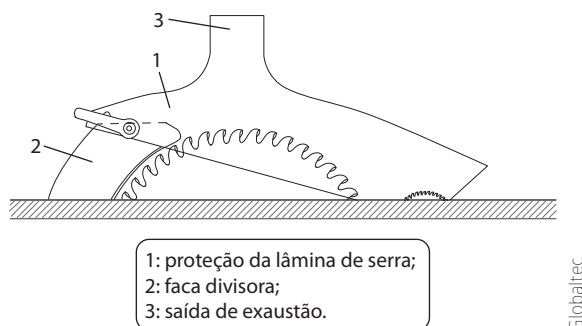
Exemplo de proteção da lâmina de serra montada na faca divisora
